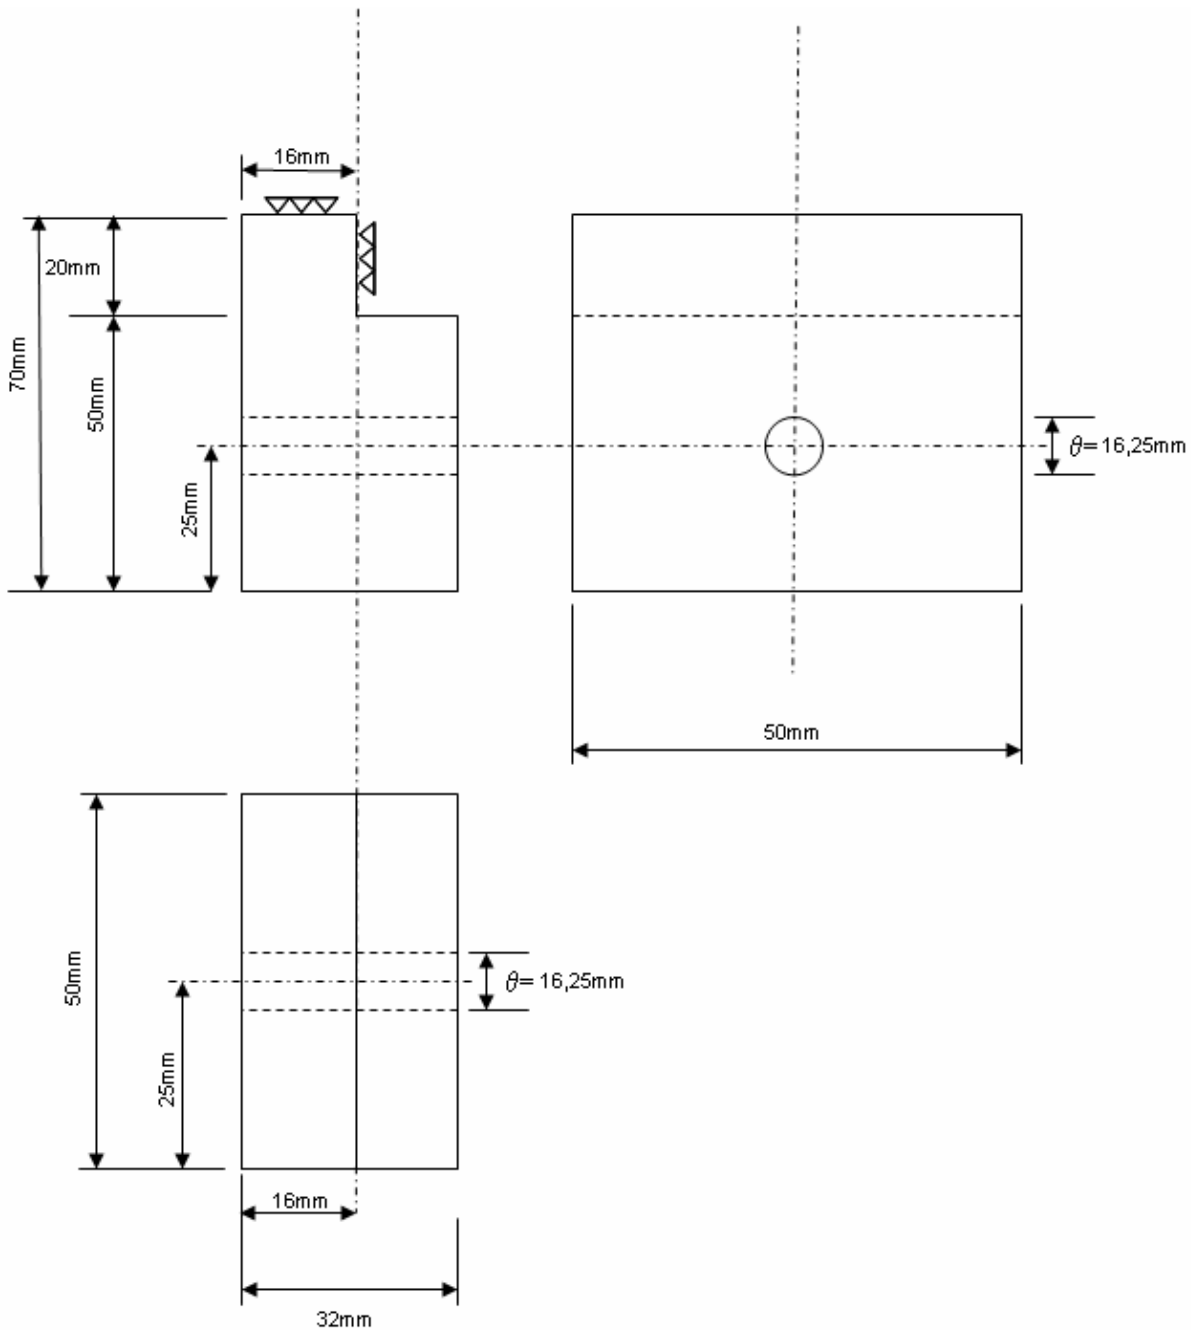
Desenho da ferramenta de corte projetada para o experimento em laboratório.
